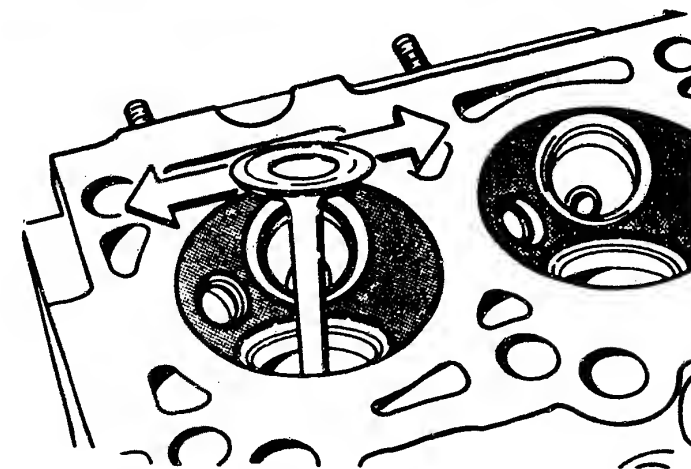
CVH-Motor: Bei 25...30mm herausgehobenem Ventil wird durch seitliches Hin- und Herbewegen am Tellerrand das Führungsspiel gemessen.
